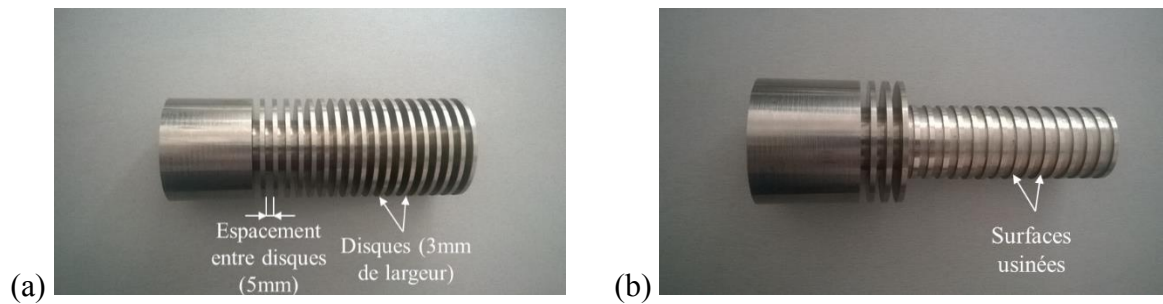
Éprouvette d'usinage. (a) Forme initiale. (b) Forme usinée.
